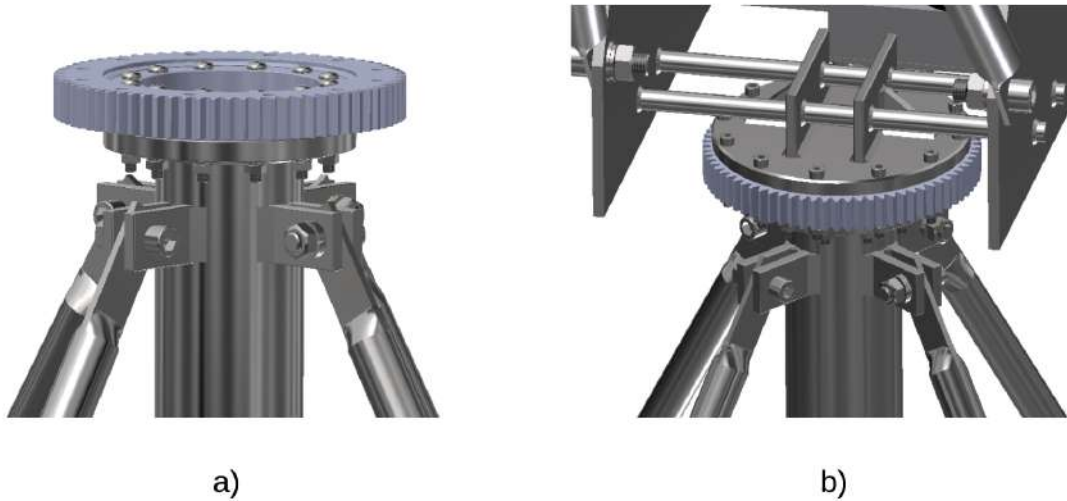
a) Ensamble Rodamiento de Giro - Columna principal. b) Ensamble general del rodamiento de giro.
